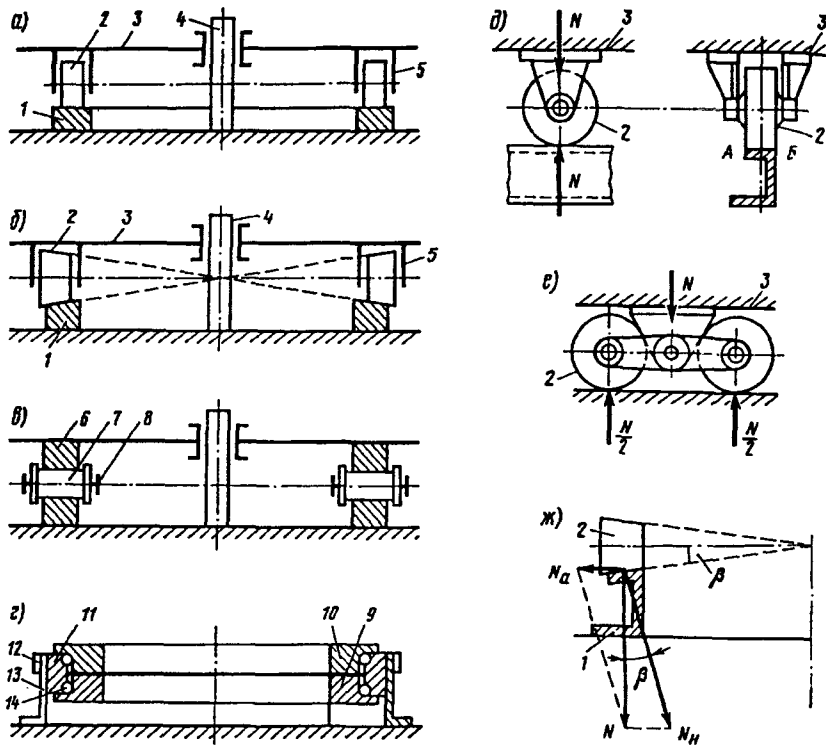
Типы опорно-поворотных устройств кранов и расчетные схемы: а, б — малоопорные с кругом катания и цилиндрическими (коническими) колесами; в — многоопорная роликовая; г — многоопорная двухрядная шариковая; д, е, ж — схемы соответственно для одинарных колес, для колес на балансирах, для конических колес
